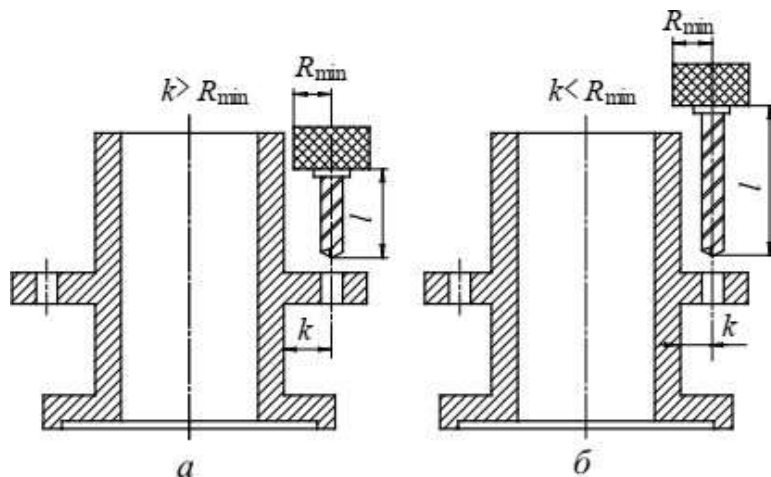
Конструкція корпусних деталей з отворами на фланці:
